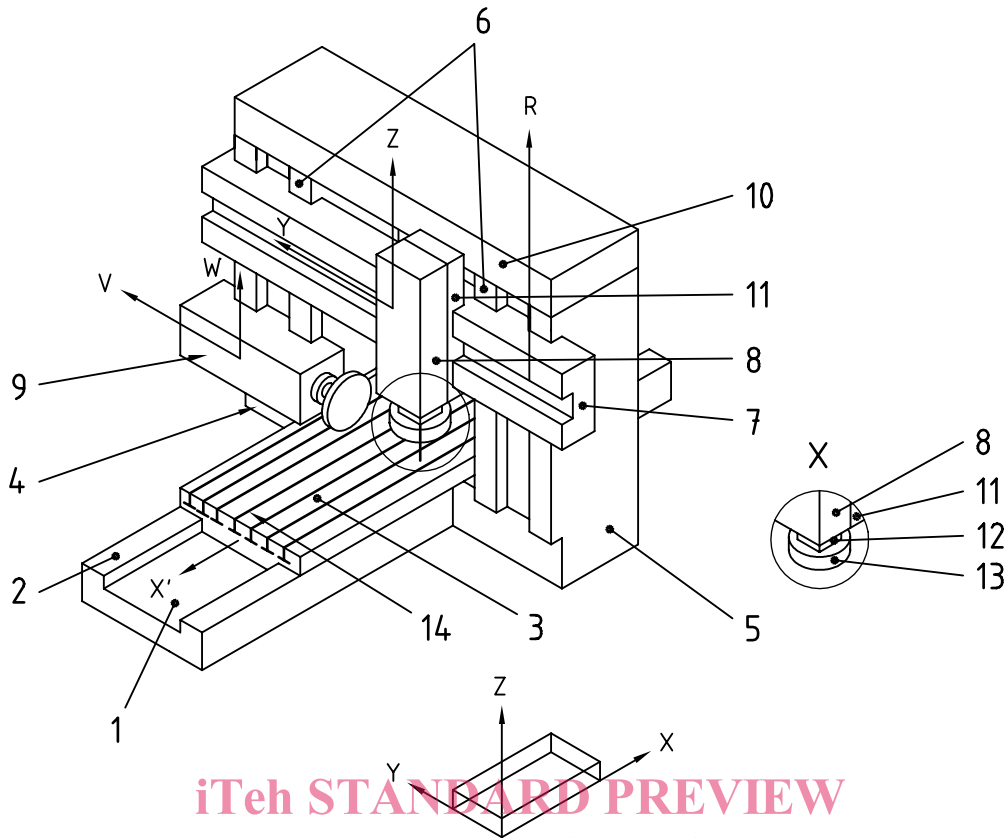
Machine à fraiser à portique fixe à traverse mobile
